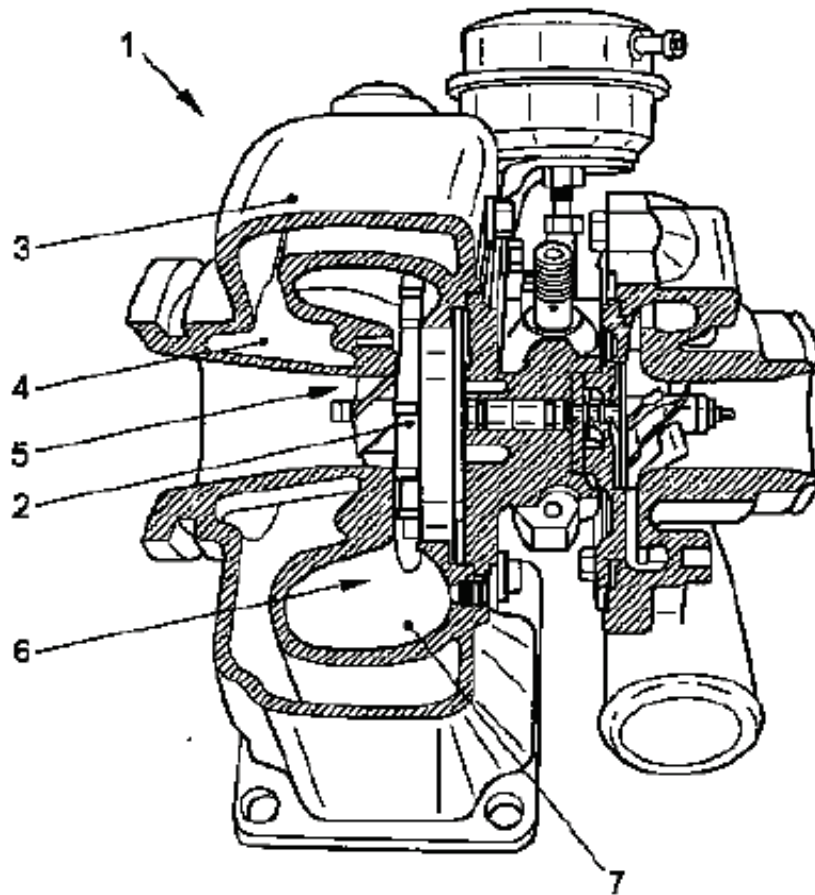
Standard VTG-Turbinengehäuse [2]
